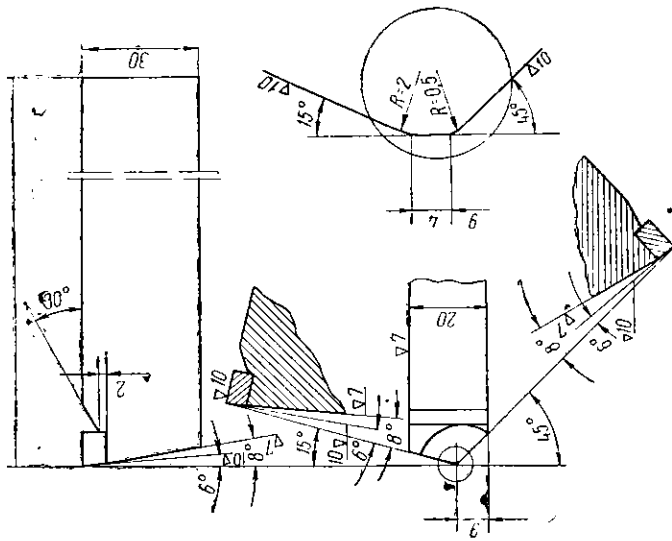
Конструкция зуба развертки с твердосплавной пластиной.
